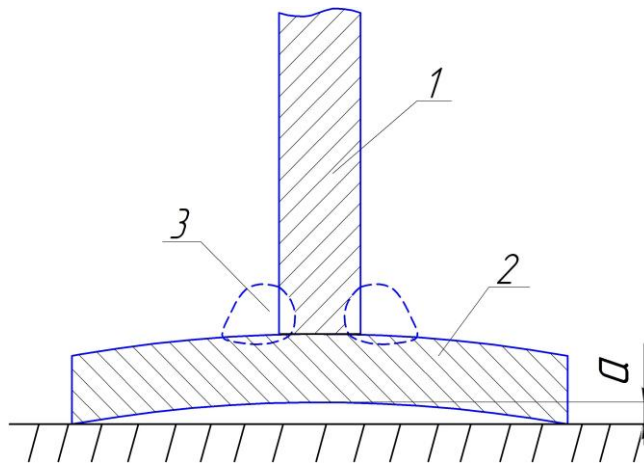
Величина деформации образцов до и после сварки
